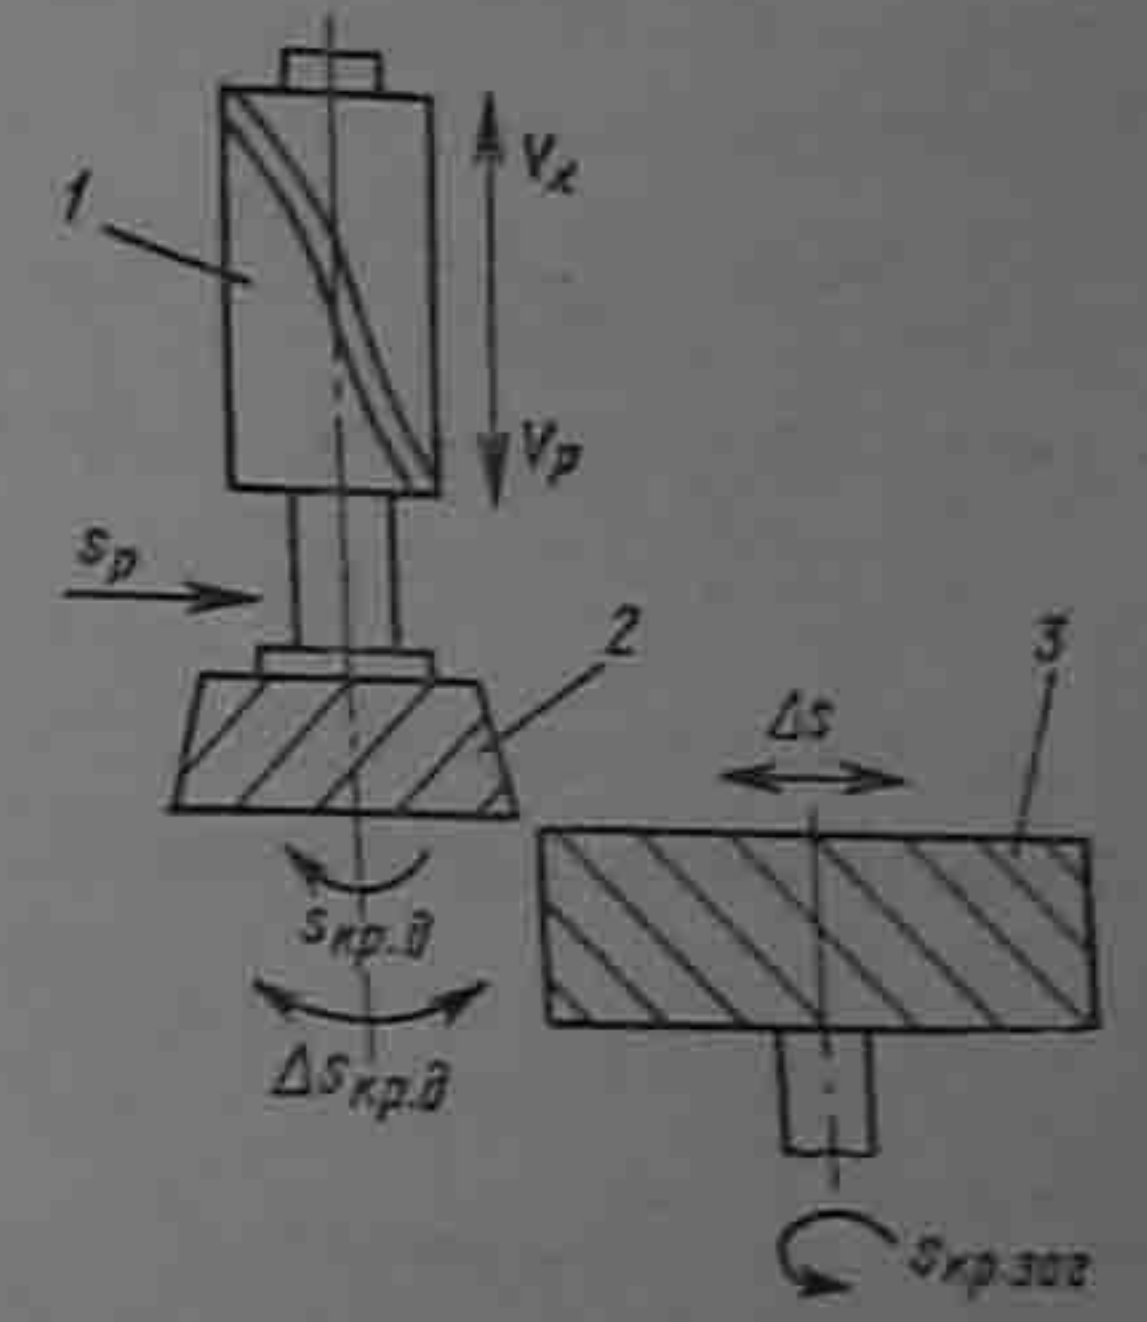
Схемы нарезания цилиндрического колеса с косыми зубьями внешнего зацепления на зубодолбежном станке: 1 — копир; 2 — долбьяк; 3 — нарезаемое колесо
